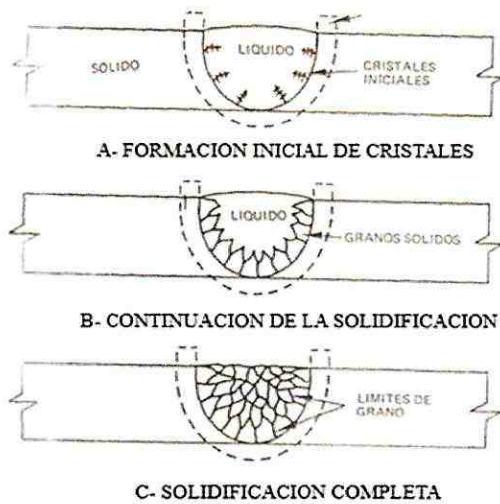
Etapas de la solidificación de un metal en la soldadura.
